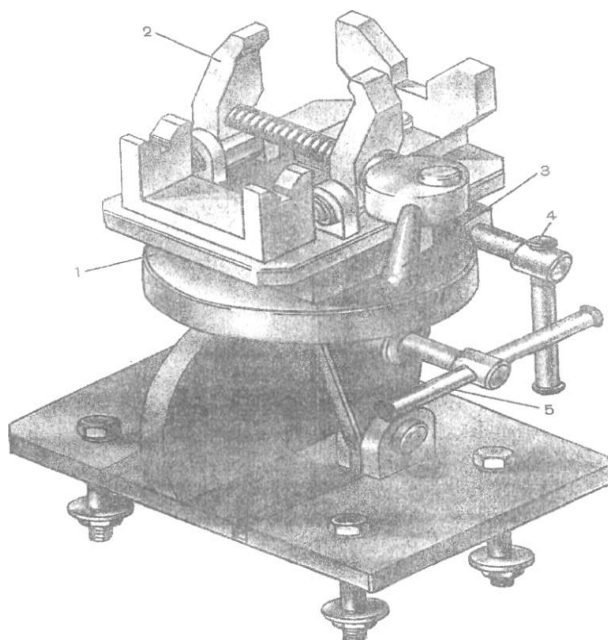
Загальний вигляд пристрою для розбирання насосів типу НД: 1 – поворотний стіл; 2 – гнучкі лещата; 3 – ручка ексцентрика; 4 – рукоятка для фіксації насосу; 5 – рукоятка для нахилу поворотного столу.
